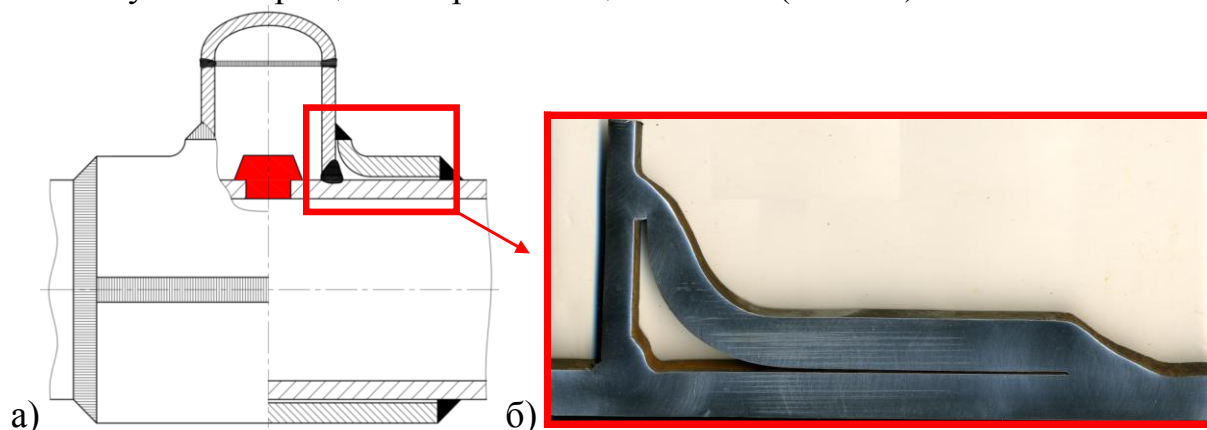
Испытания патрубкового тройника: а) конструкция тройника; б) макро-шлиф сварного соединения
